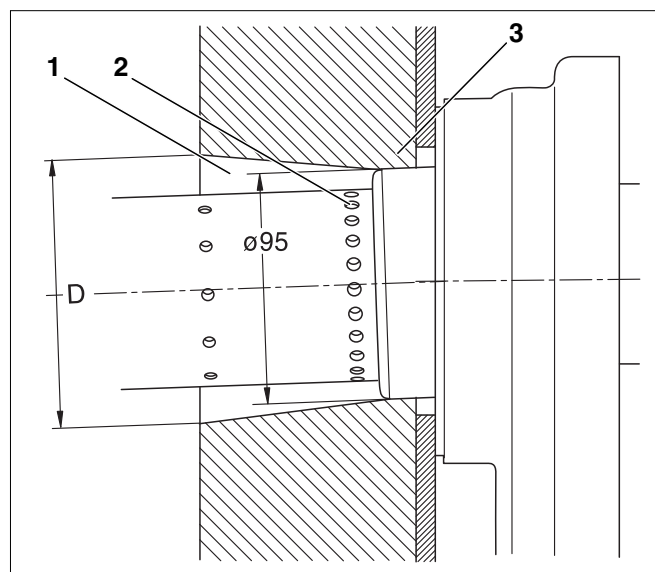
Esquema de corte de la sección de la puerta (medida en mm)
